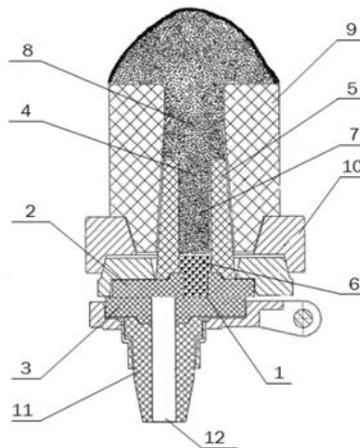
Способ подготовки шиберного затвора сталеразливочного ковша
